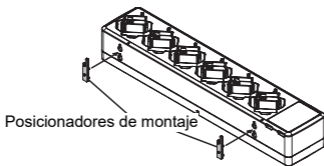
Instalación de posicionadores de montaje en orificios de montaje
